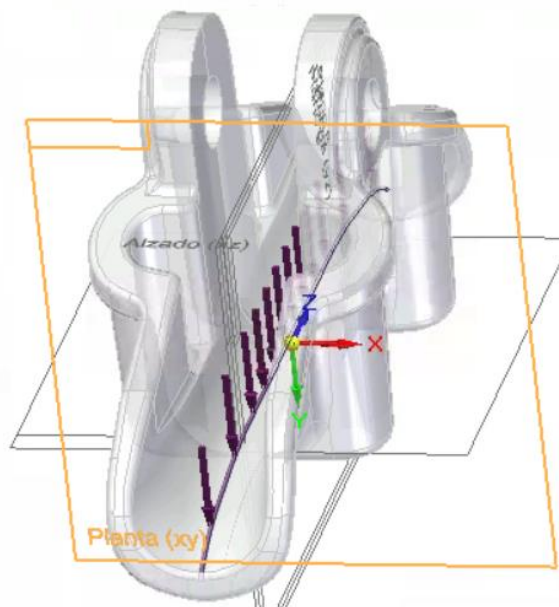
Detalle fuerza. Fuente: elaboración propia
